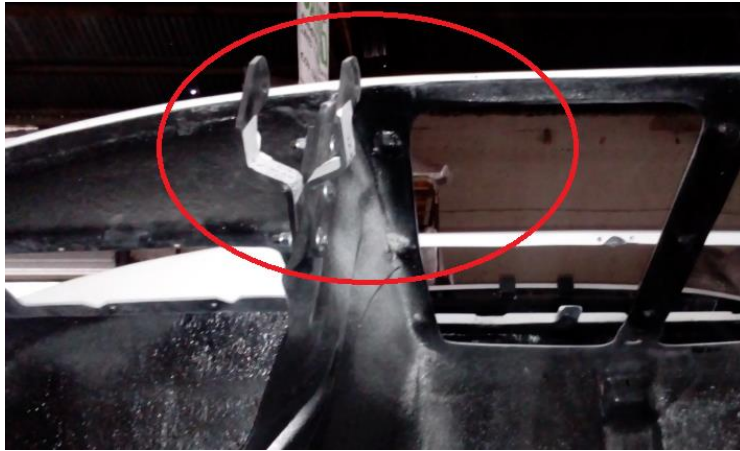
(Herraje terminado y ensamblado en cofre terminado)
